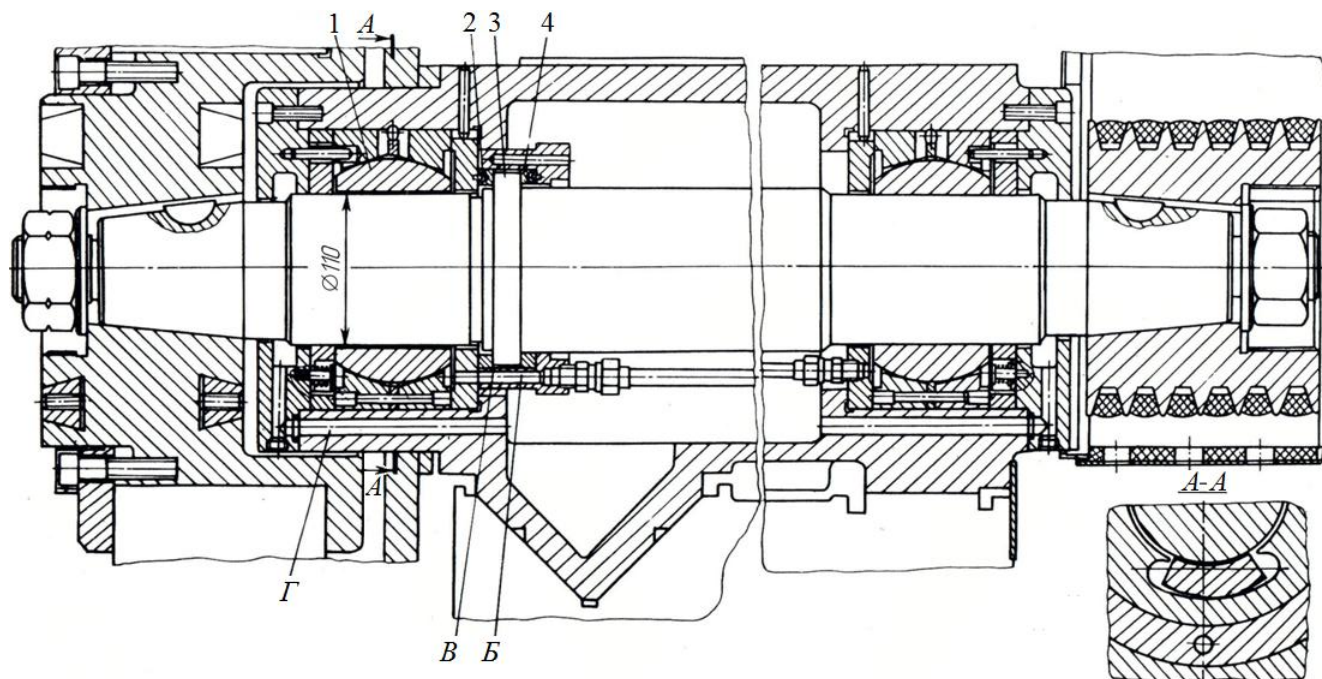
Шпиндельный узел шлифовального станка с гидродинамическими опорами
